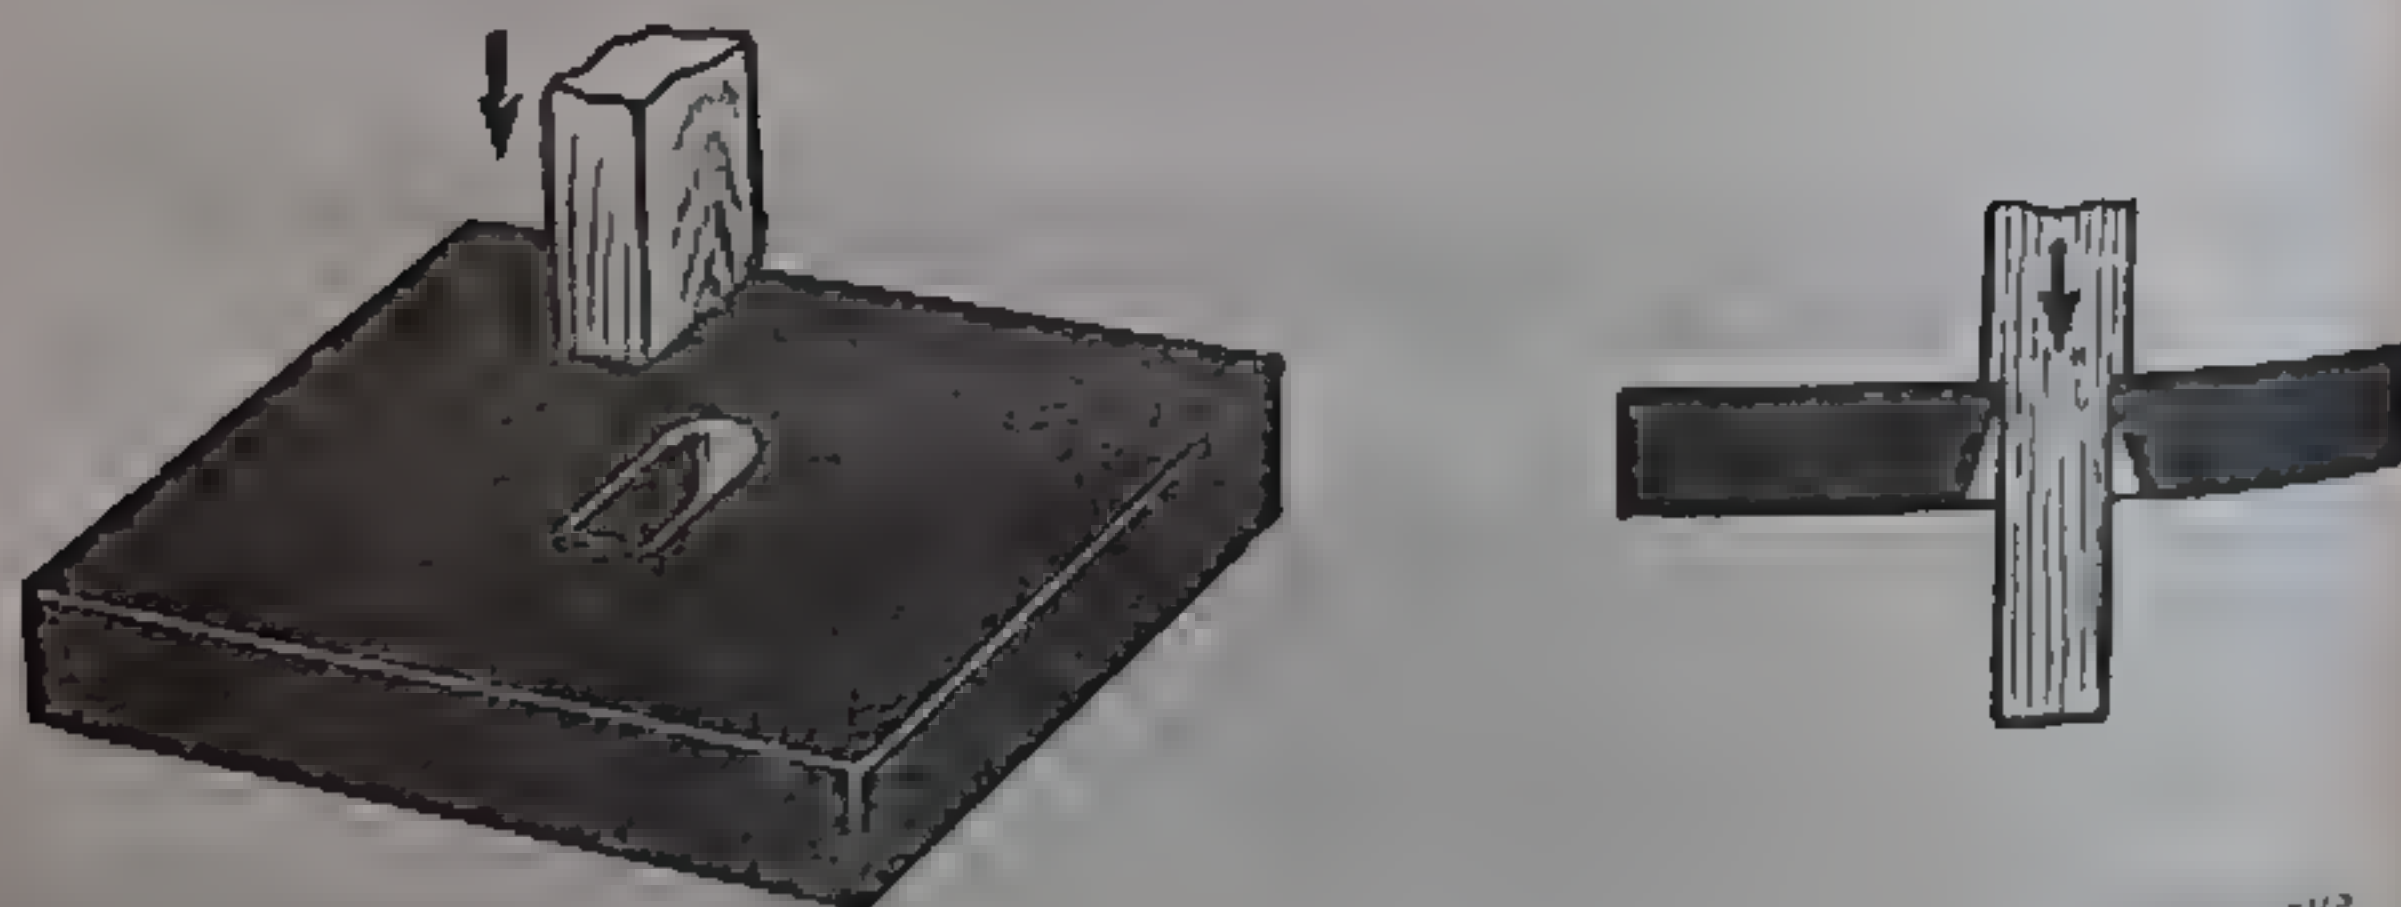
Пробивка брусочков через калибровочное отверстие.
